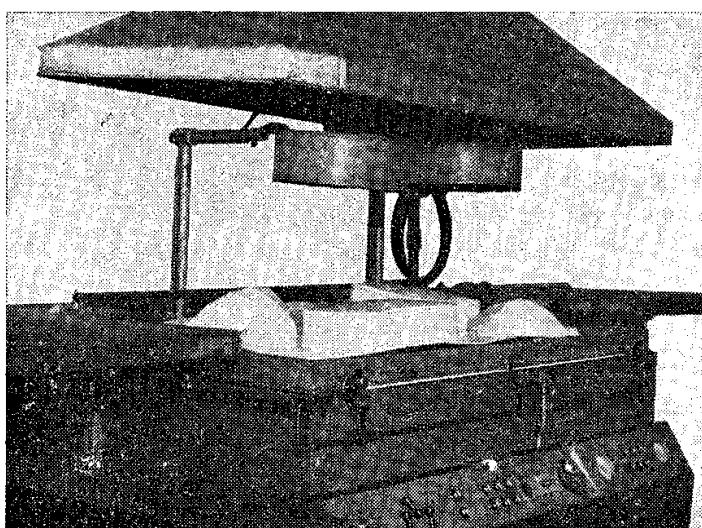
Формование корпусов гитар, балалаек из пластмассы на вакуум-формовочной машине
